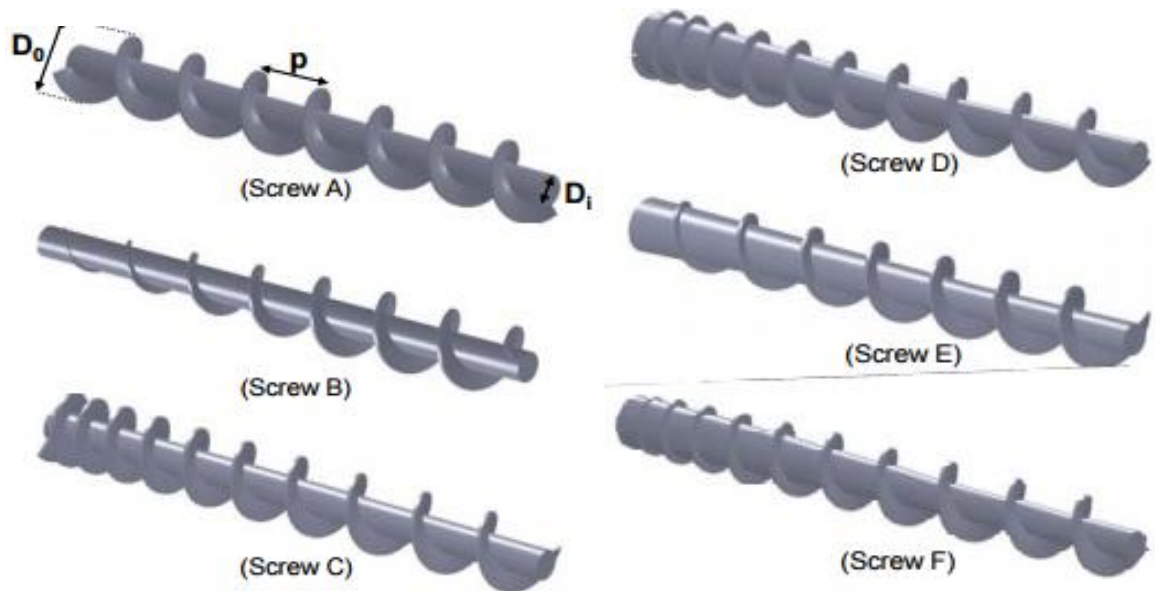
Конструкції шести різних гвинтових робочих органів: Screw A – стандартний гвинтовий робочий орган із зовнішнім діаметром витків  $D_0$ , внутрішнім діаметром витків  $D_1$  та кроком витків  $p$ ; Screw B – гвинтовий робочий орган із конічними витками; Screw C – гвинтовий робочий орган із змінним кроком витків; Screw D – гвинтовий робочий орган із конічним валом та змінним кроком витків; Screw E – гвинтовий робочий орган із конічними витками та валом; Screw F – гвинтовий робочий орган із зростаючим діаметром витків по параболі, конусним валом та змінним кроком витків [179]
